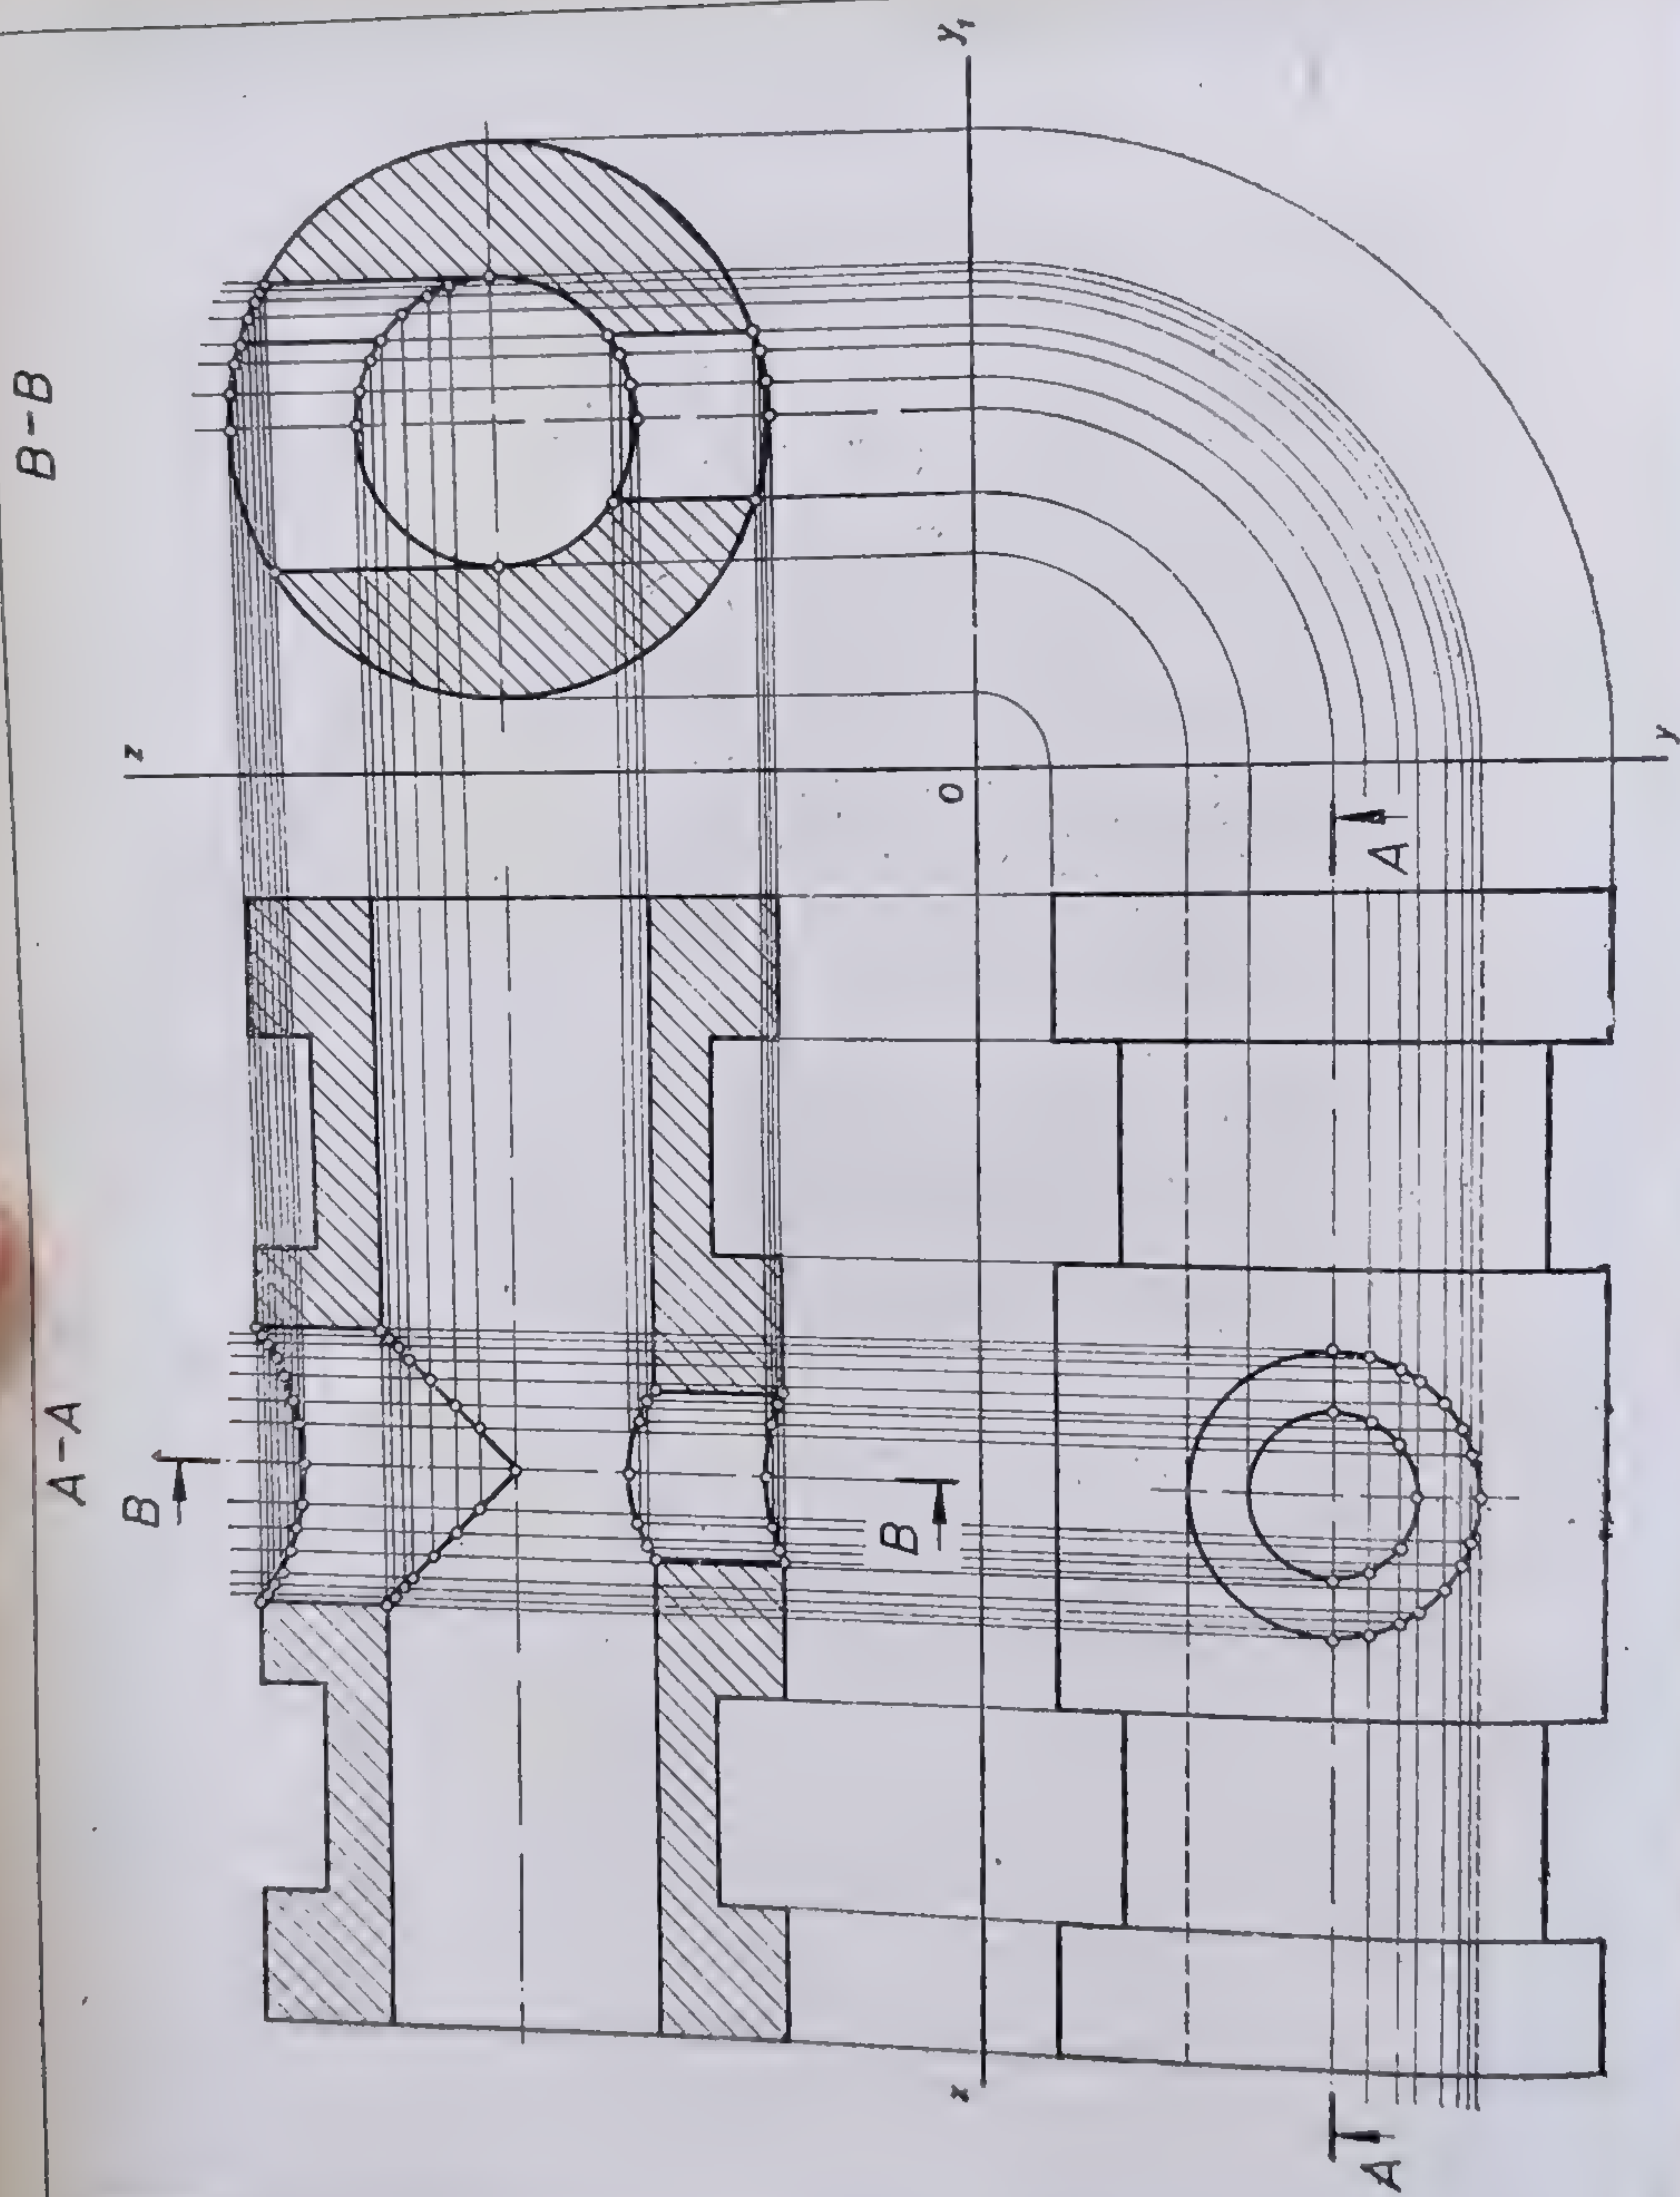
Formă constructivă de rotație prevăzută cu o gaură cilindrică longitudinală care se intersectează cu două găuri
